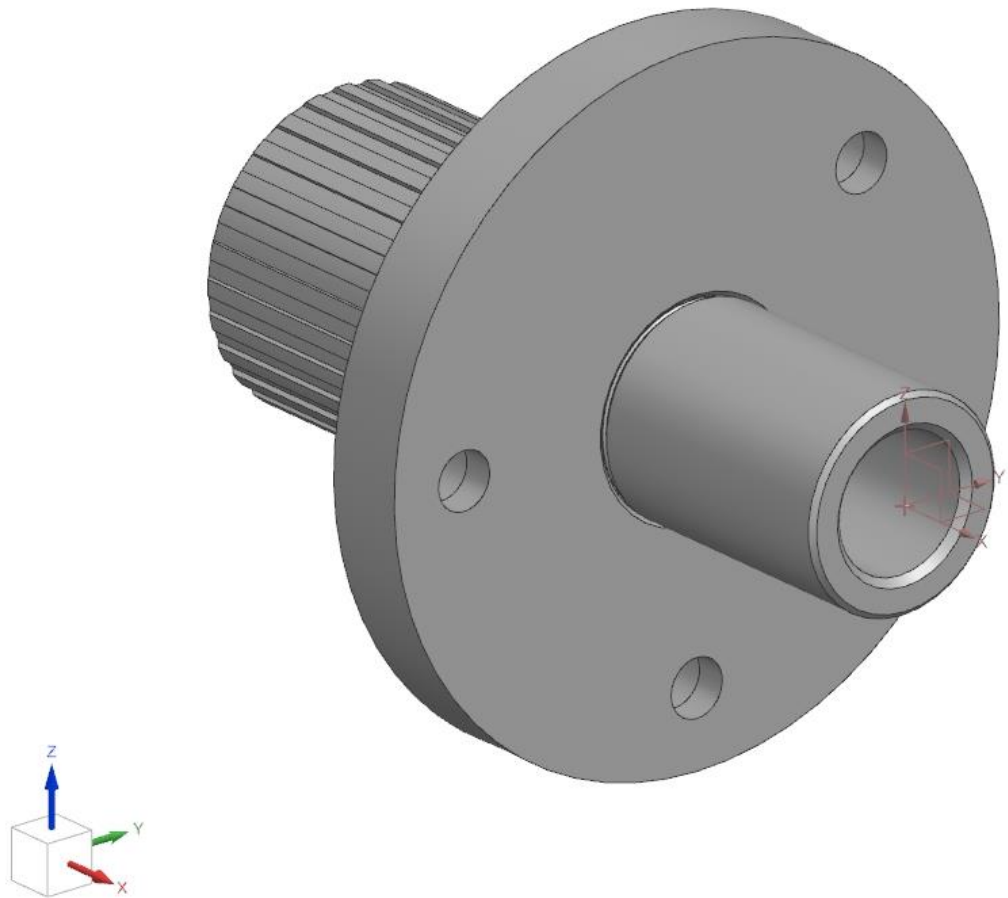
Створення 3д моделі деталі до обробки
